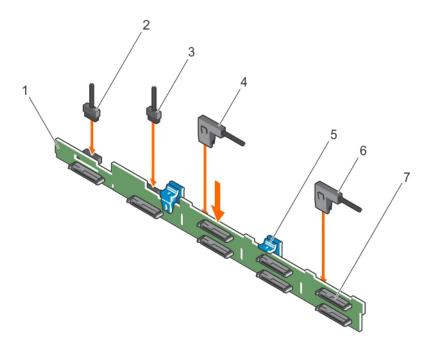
Installation du fond de panier des huit SAS/SATA de 2,5 pouces
